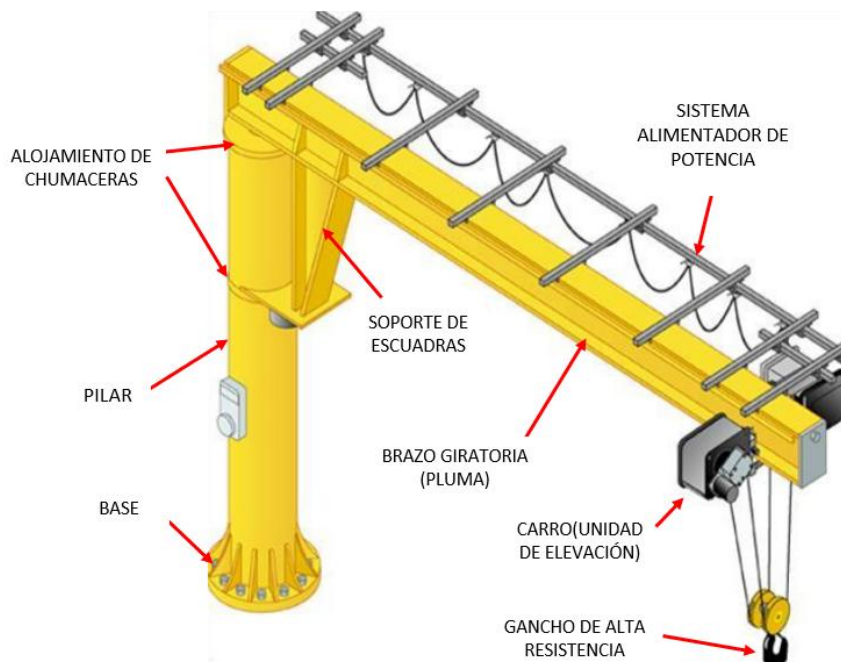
Partes de la grúa pescante tipo columna (Jib crane)
